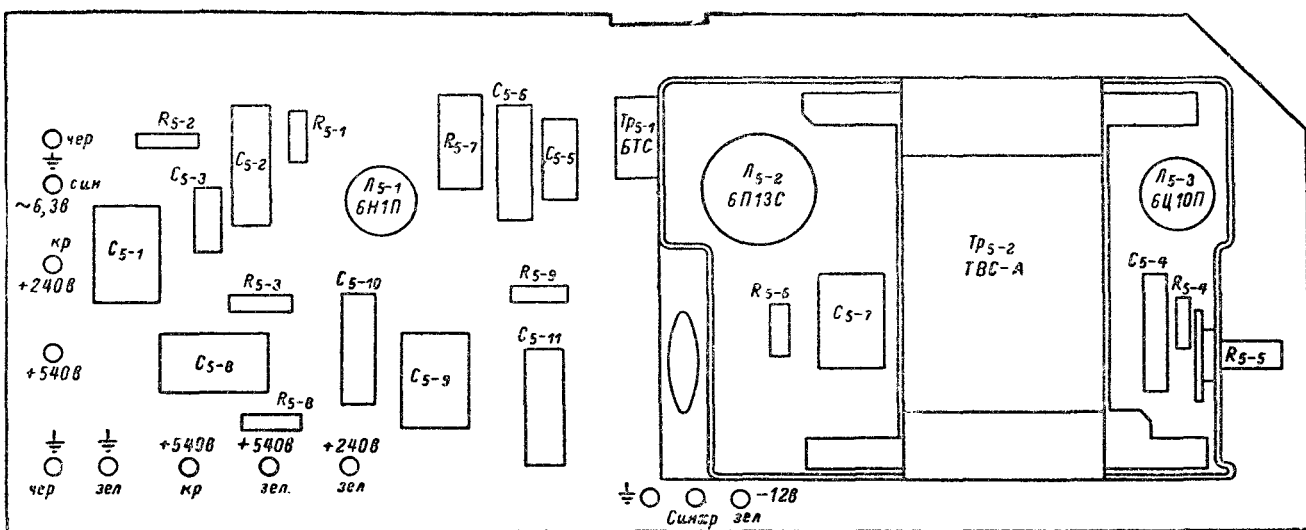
Расположение деталей на плате строчной развертки телевизора «Нева».
